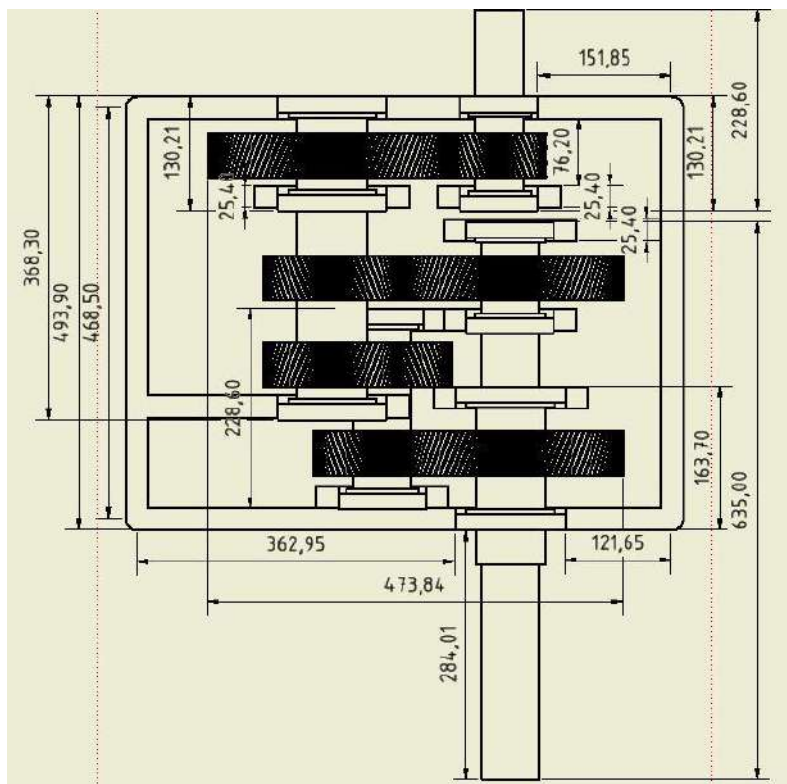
Tampak Samping pada Sistem Transmisi Alternatif 1
